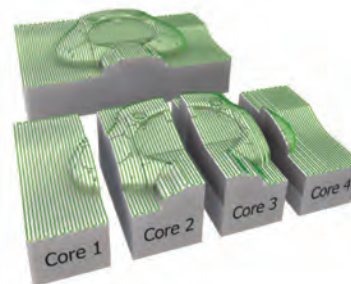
Příklad pětiosé hrubovací operace - PowerMILL
